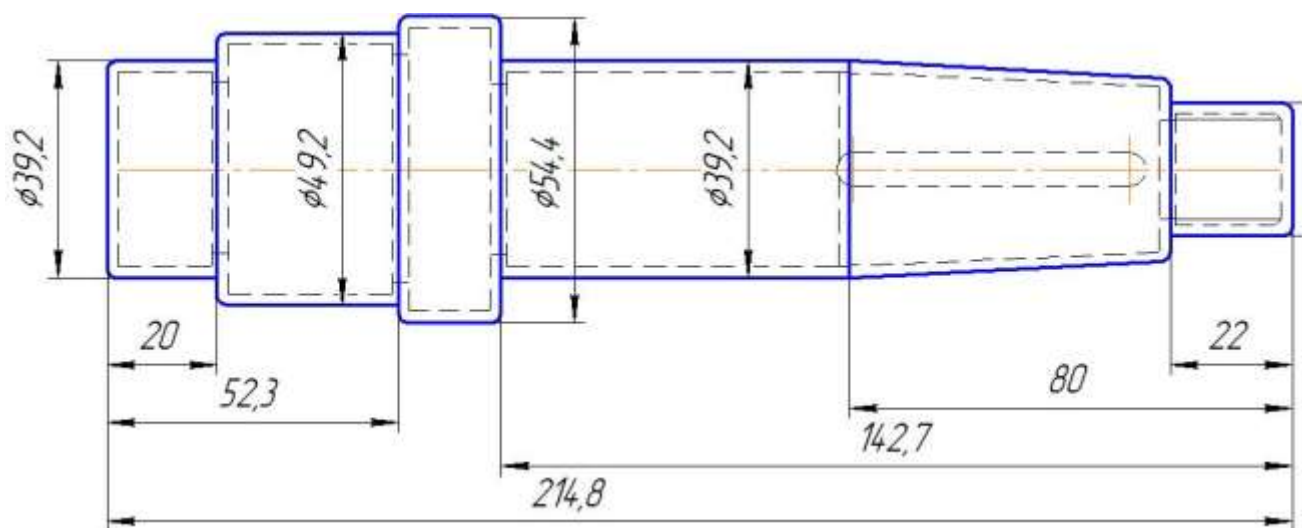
Заготовка отримана штампуванням на КГШП
